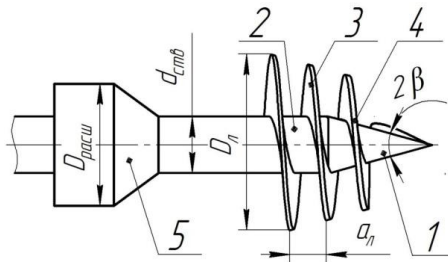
Конструкція гвинтового проколювального робочого органу: 1 – наконечник; 2 – основна гвинтова лопать; 3 – штанга; 4 – додаткова тягова лопать; 5 – розширювальний конус
